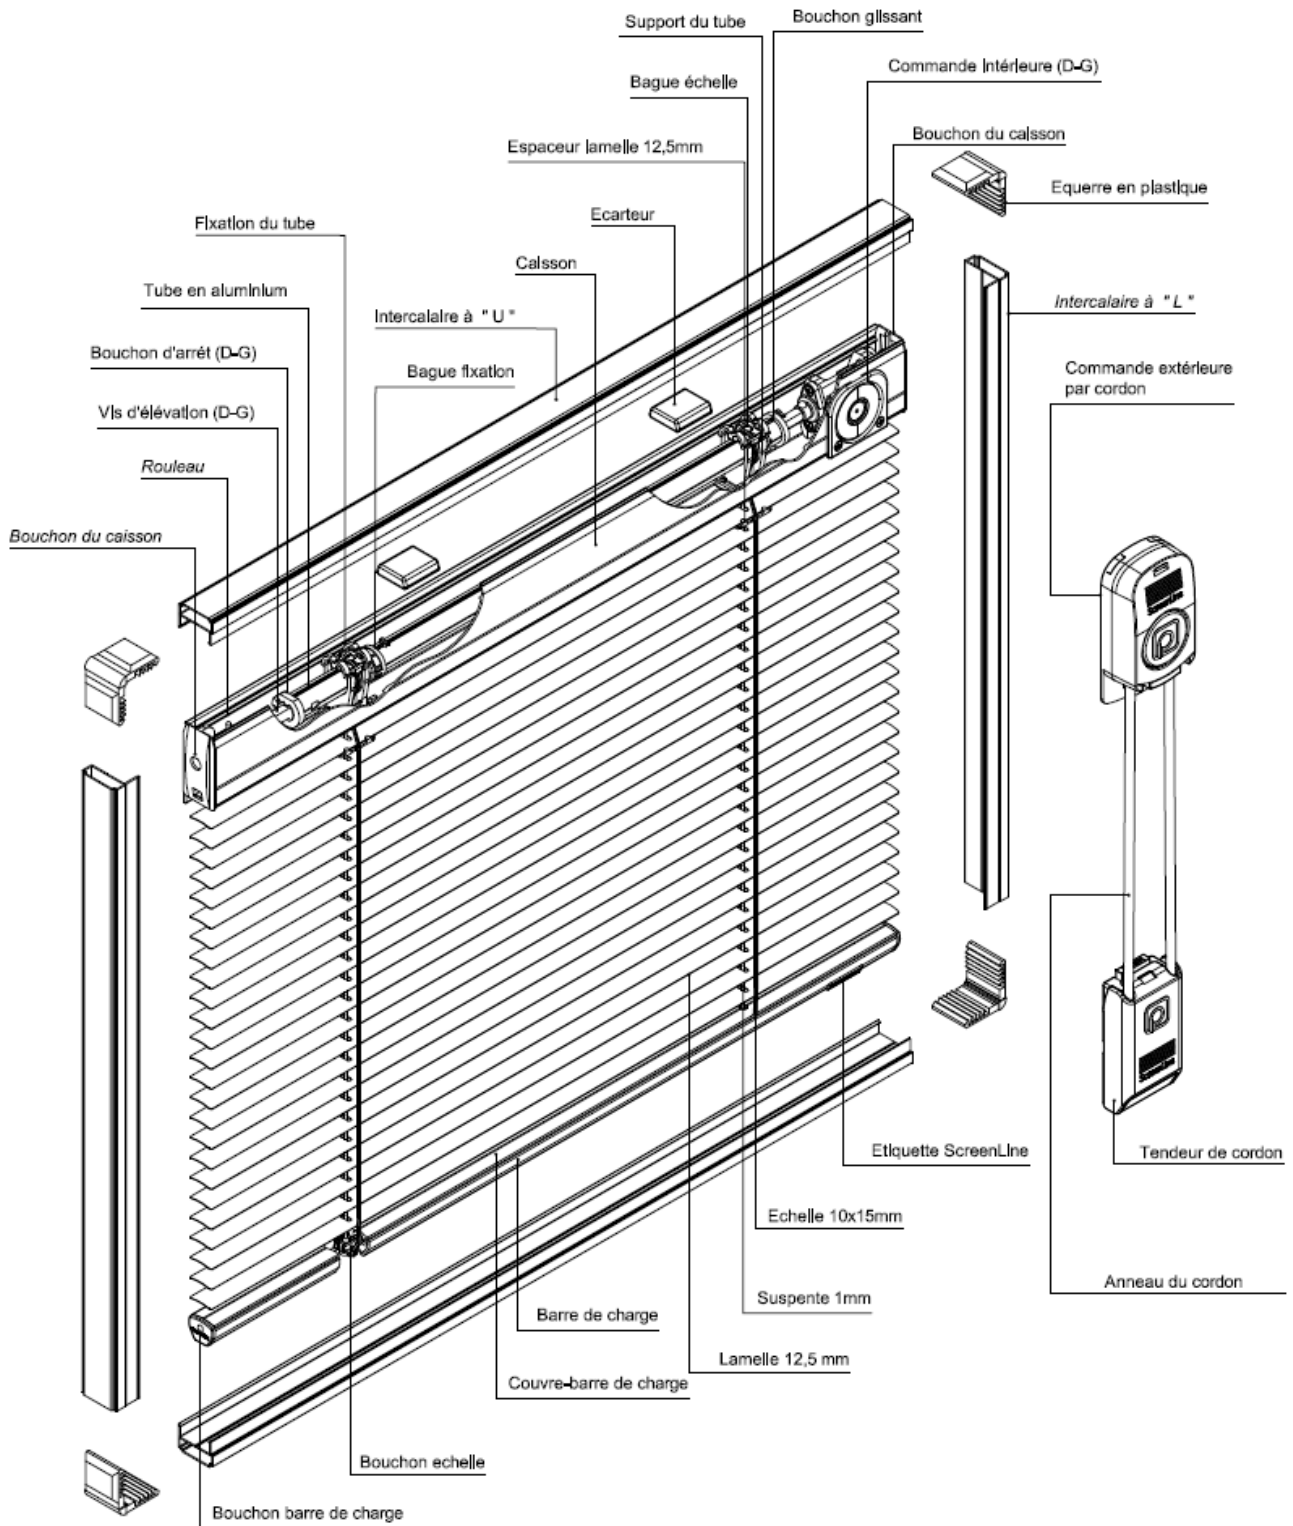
a – Vue d'ensemble éclatée - Store avec espaceur aluminium en position basse
